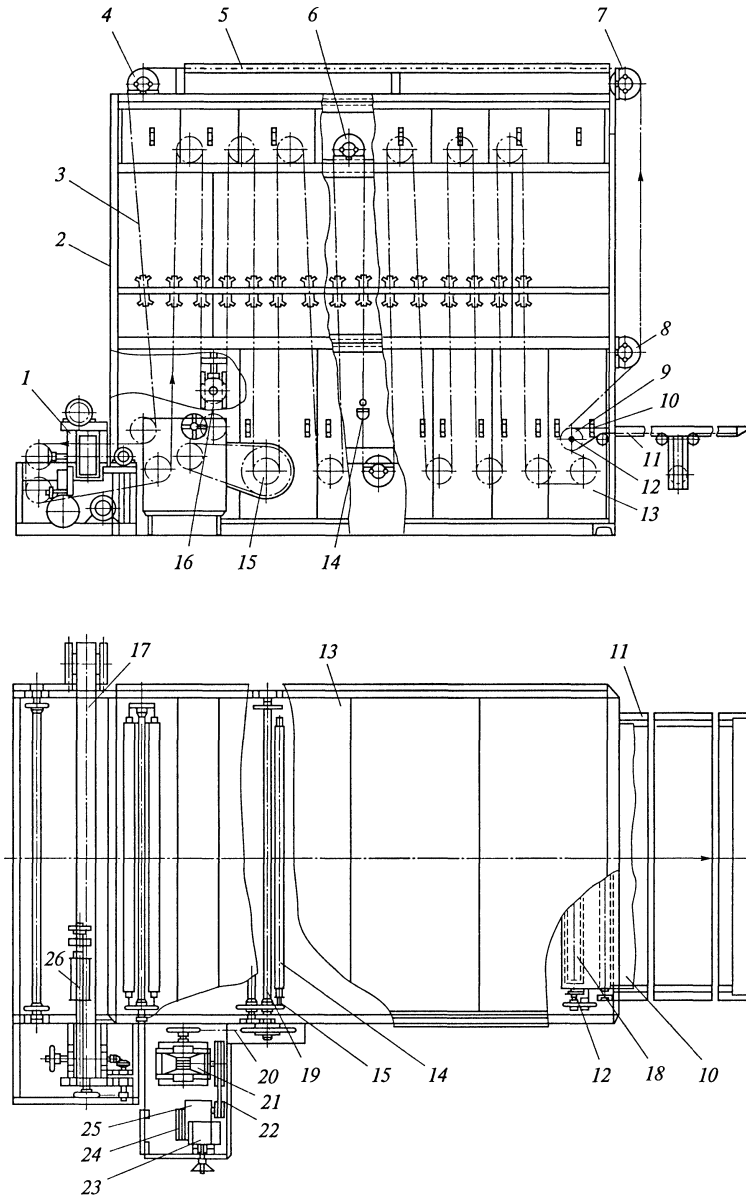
Шкаф РШВ для расстойки заготовок мелкоштучных и хлебных изделий
